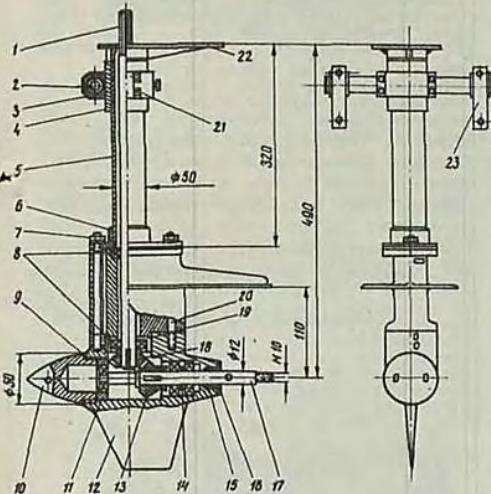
Модернизированная подводная часть мотора «Москва» и узел крепления: 1 — вал; 2 — труба подвески; 3 — кронштейн подвески; 4 — втулка; 5 — дейдвудная труба; 6 — фланец; 7 — шпилька; 8 — подшипники № 60201; 9 — прокладка; 10 — пробка; 11 — подшипниковая втулка; 12 — киль; 13 — шестерня гребного вала; 14 — распорные шайбы; 15 — уплотнение; 16 — втулка; 17 — гребной вал; 18 — шестерня; 19 — втулка подшипниковая; 20 — шпилька; 21 — крышка; 22 — плита; 23 — кронштейн.
